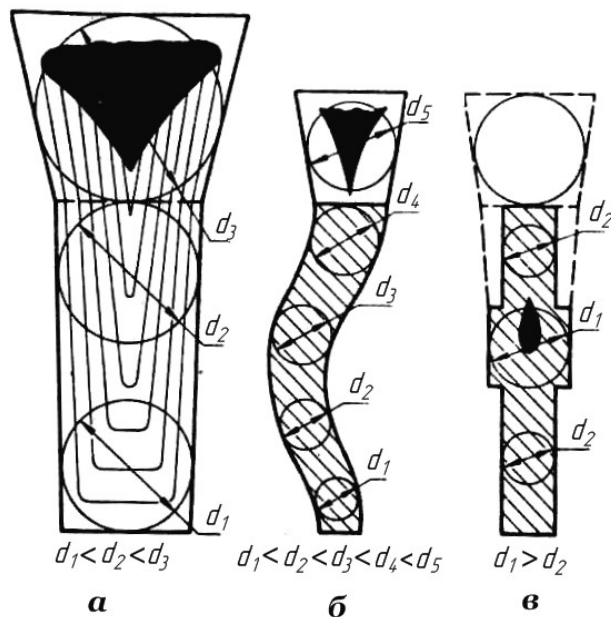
Конструкции стенок отливок: а, б – обеспечивающие направленное затвердевание; в – не обеспечивающая направленного затвердевания
